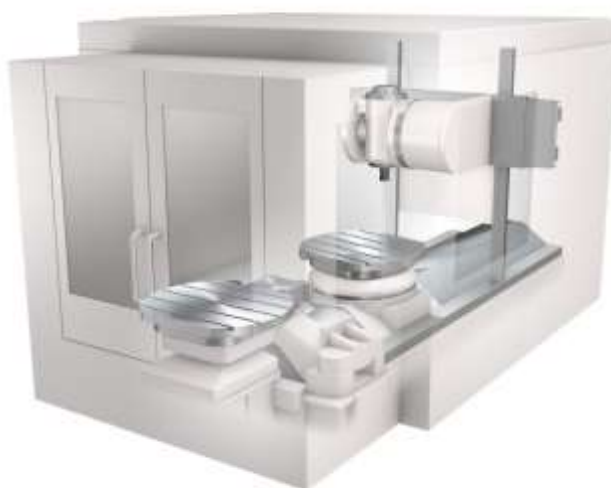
Фрезерный станок с ЧПУ с дополнительной паллетой
